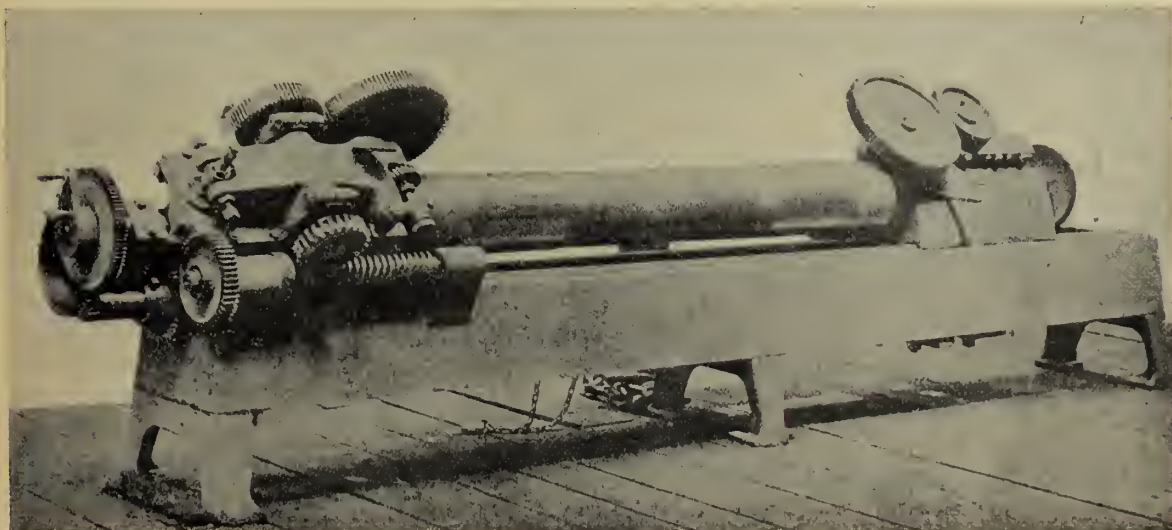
Machine à fraiser les logements de clavettes dans les essieux de locomotives, ateliers *Brooks*.
